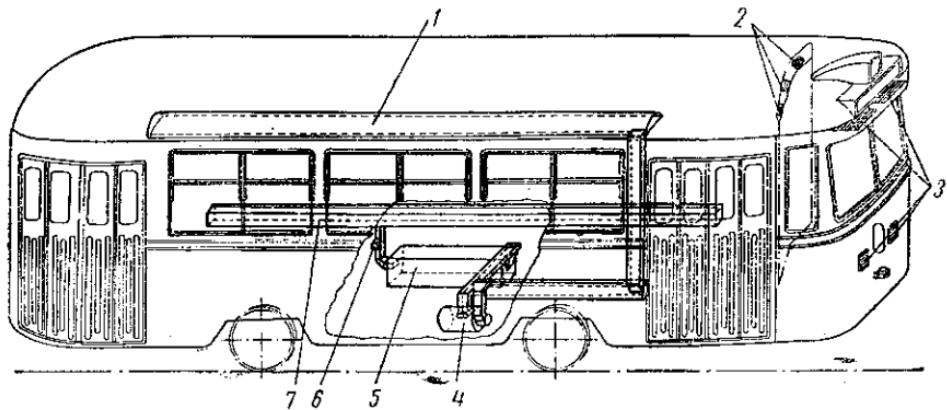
Схема вентиляции и отопления вагона КТМ-2:
